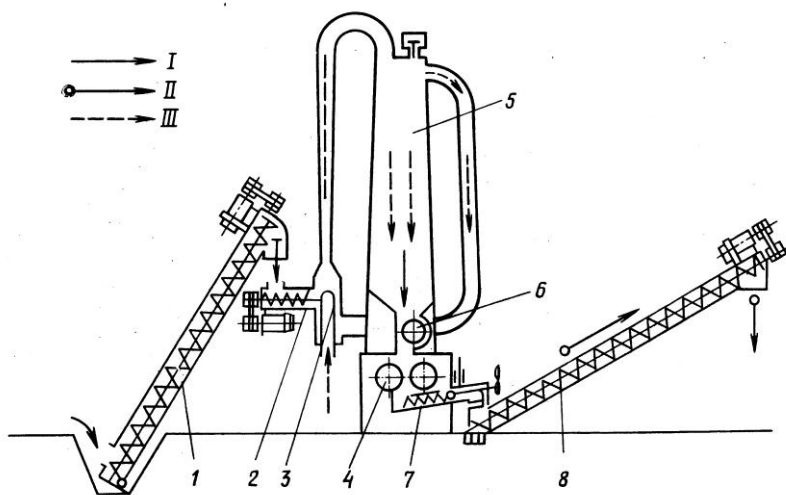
Схема технологического процесса агрегата ПЗ-3А: 1 — загрузочный шнек; 2 — шнек-эжектора; 3 — эжектор; 4 — плющилка; 5 — пропариватель; 6 — дозатор; 7 — шнек плющилки; 8 — шнек выгрузной; I — зерно; II — хлопья; III — пар
